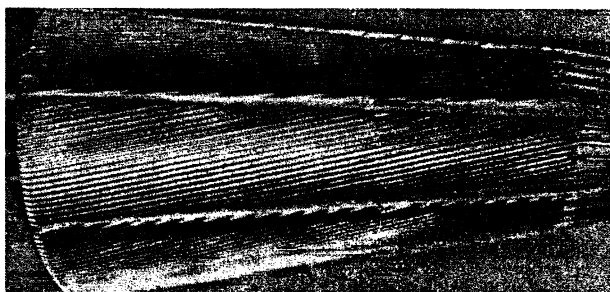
Нож конической мельницы, обработанный ротационным резцом
